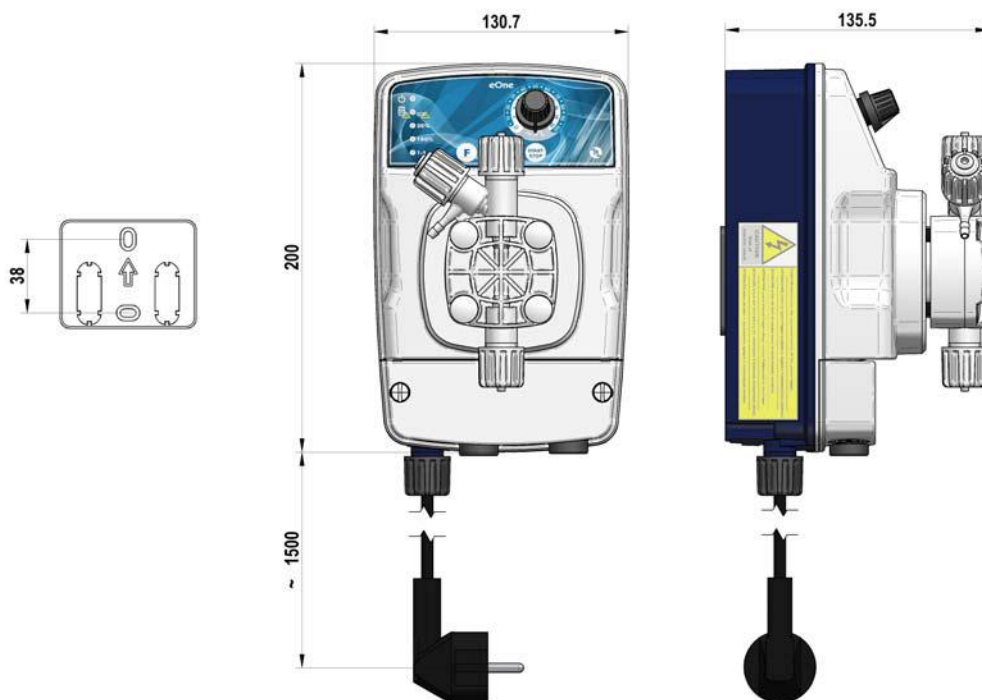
Dimensioni in mm. Placca per il fissaggio a parete.
